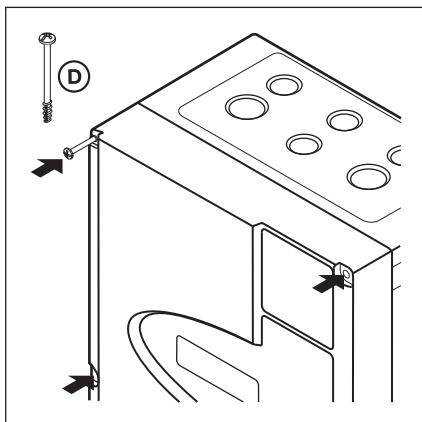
Alle Deckelschrauben (6x) montieren
